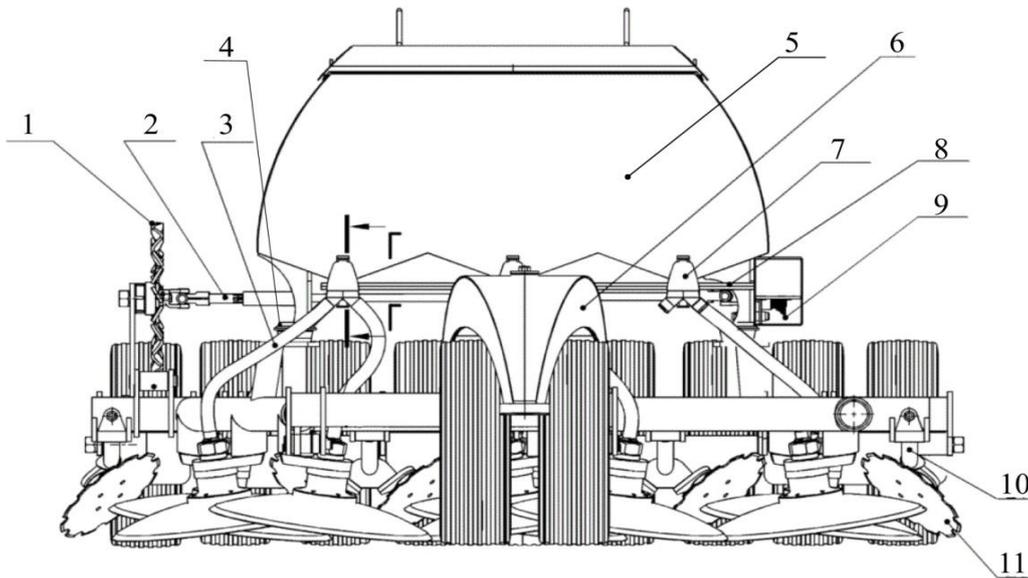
Визуализация электронной модели сеялки (вид спереди): 1 – диск привода высевающего аппарата; 2 – карданный вал; 3 – семяпровод; 4 – пятка для амортизатора; 5 – бункер; 6 – сцепка; 7 – дозатор высевающего аппарата; 8 – шестигранный вал привода; 9 – редуктор; 10 – стойка; 11 – загорточ
